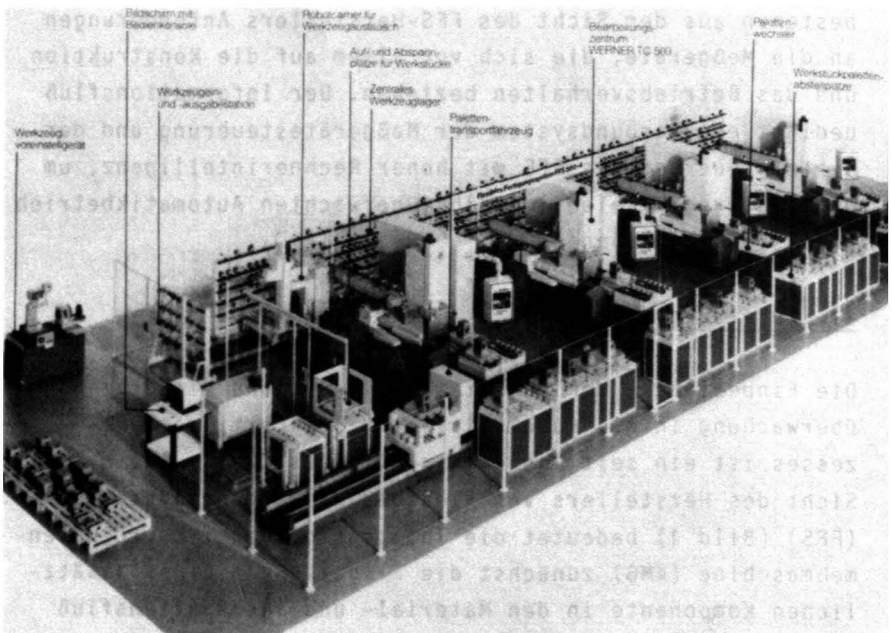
Flexibles Fertigungssystem für die Bohr- und Fräsbearbeitung (Werkbild: WERNER und KOLB Werkzeugmaschinen GmbH, Berlin)
